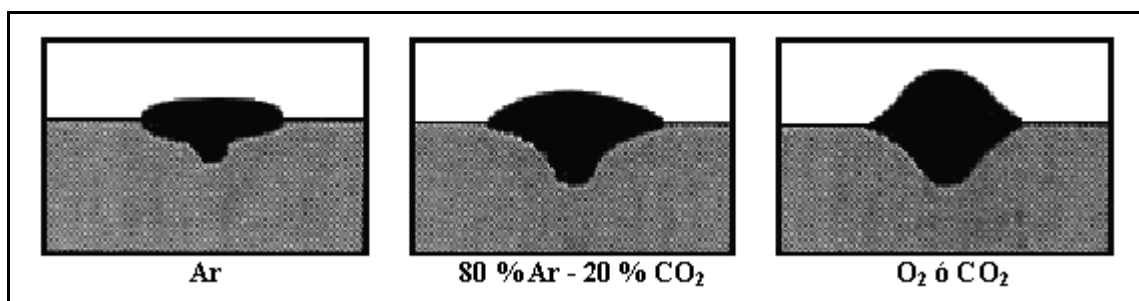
Penetración y perfil del cordón de soldadura utilizando diferentes gases de protección.
